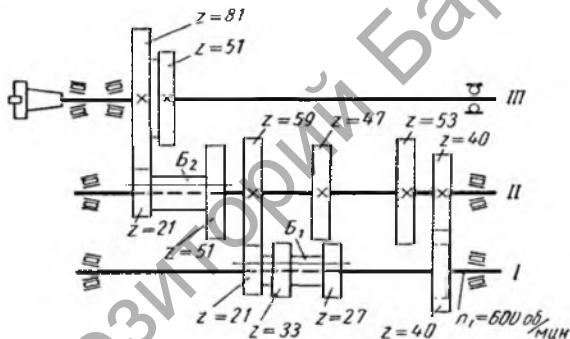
Коробка скоростей с передвижными блоками колес
